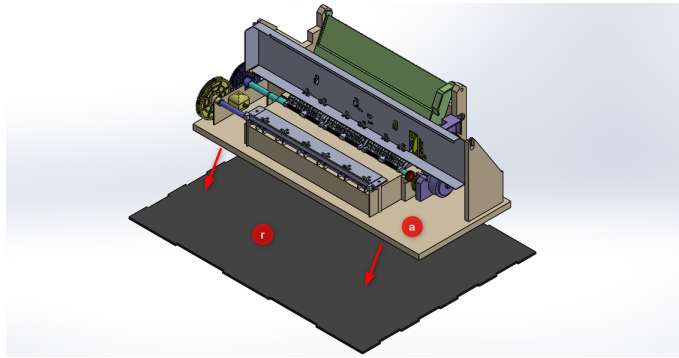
Montaje del sistema mecánico sobre base de la carcasa
